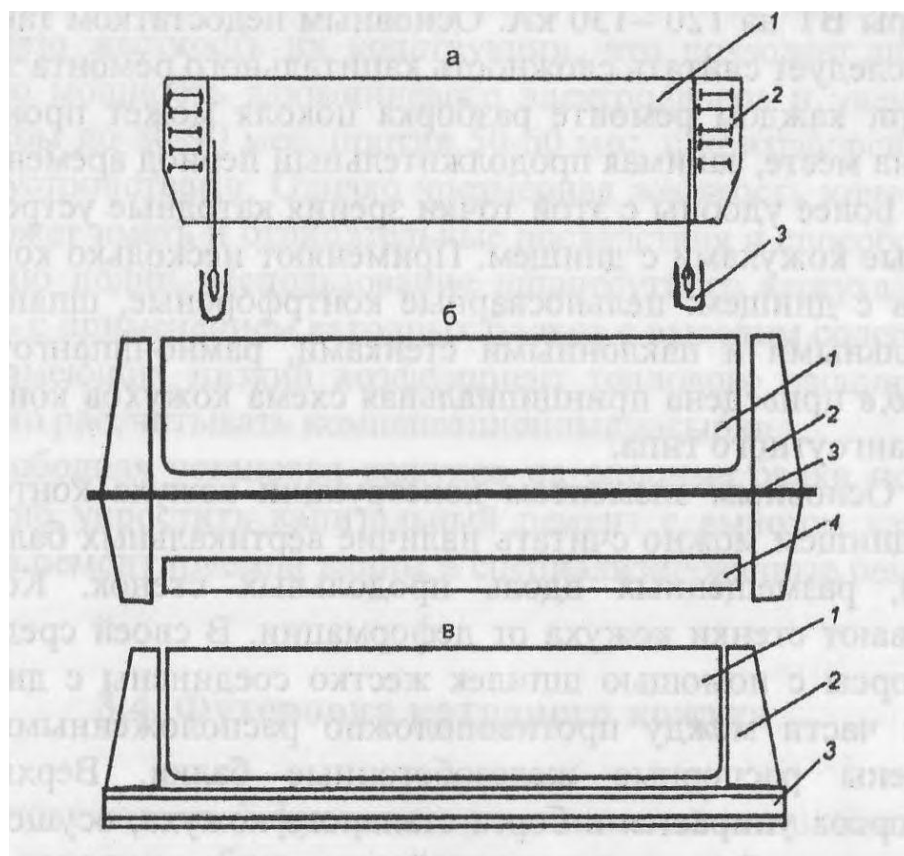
Конструкция катодных кожухов: а – рамный кожух без дна: 1 – кожух; 2 – швеллерные балки; 3 – анкерное крепление; б – контрфорсный кожух с дном: 1 – кожух; 2 – контрфорсная балка; 3 – стягивающая шпилька; 4 – распорная балка; в – шпангоутный кожух с дном: 1 – кожух; 2 – шпангоутное устройство; 5 – распорная балка
